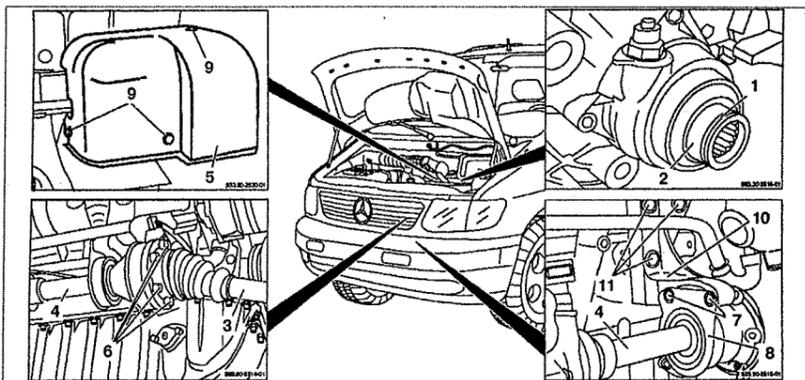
Центральный ведущий вал с подшипником (автомобили с двигателями 104.900): 1. Уплотнительное кольцо, 2. Выходной вал, 3. Правая полуось, 4. Ведущий вал, 5. Щиток, 6, 7, 9, 11. Болт, 8. Подшипник, 10. Кронштейн подшипника.
